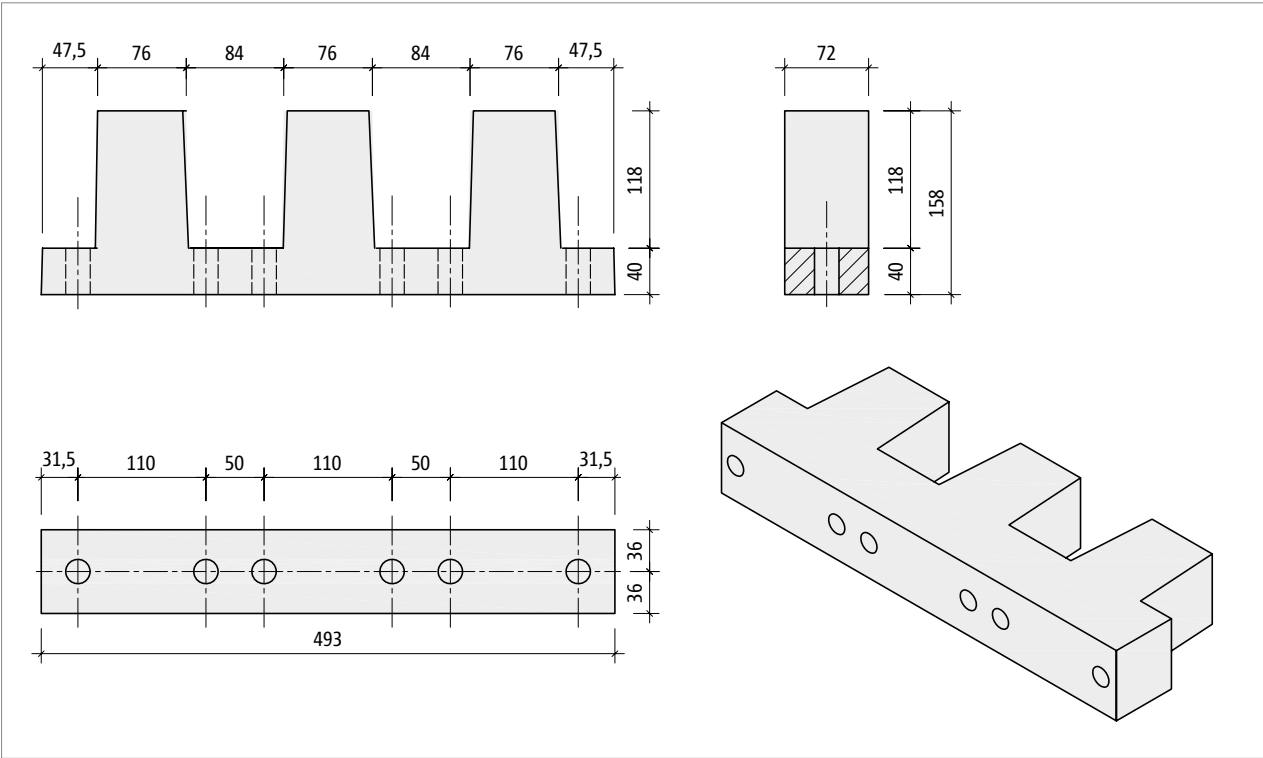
Schöck Isokorf® IQ type K-B: Bovenaanzicht
